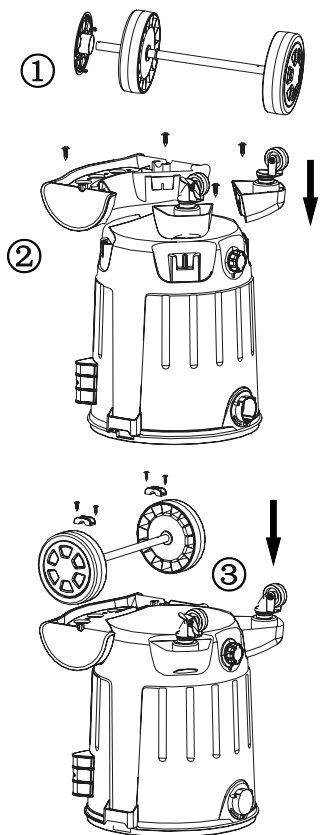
Instalação dos suportes, bases, rodas e rodízios
